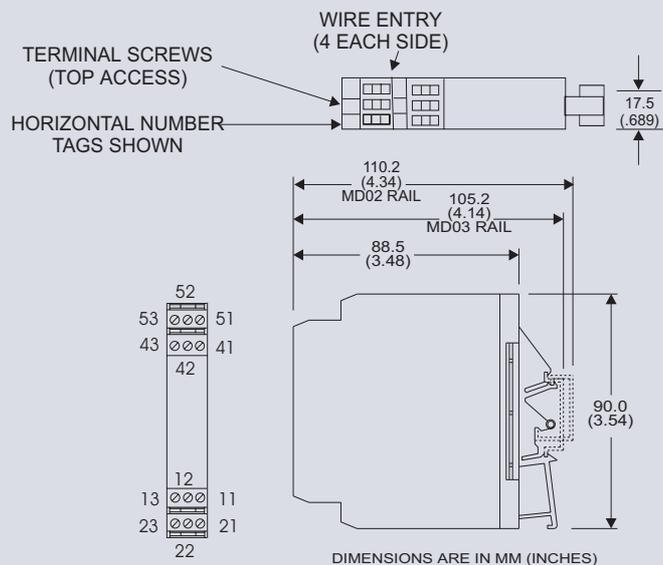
Dimensões Mecânicas do G408-0001 e do G408-1001.
